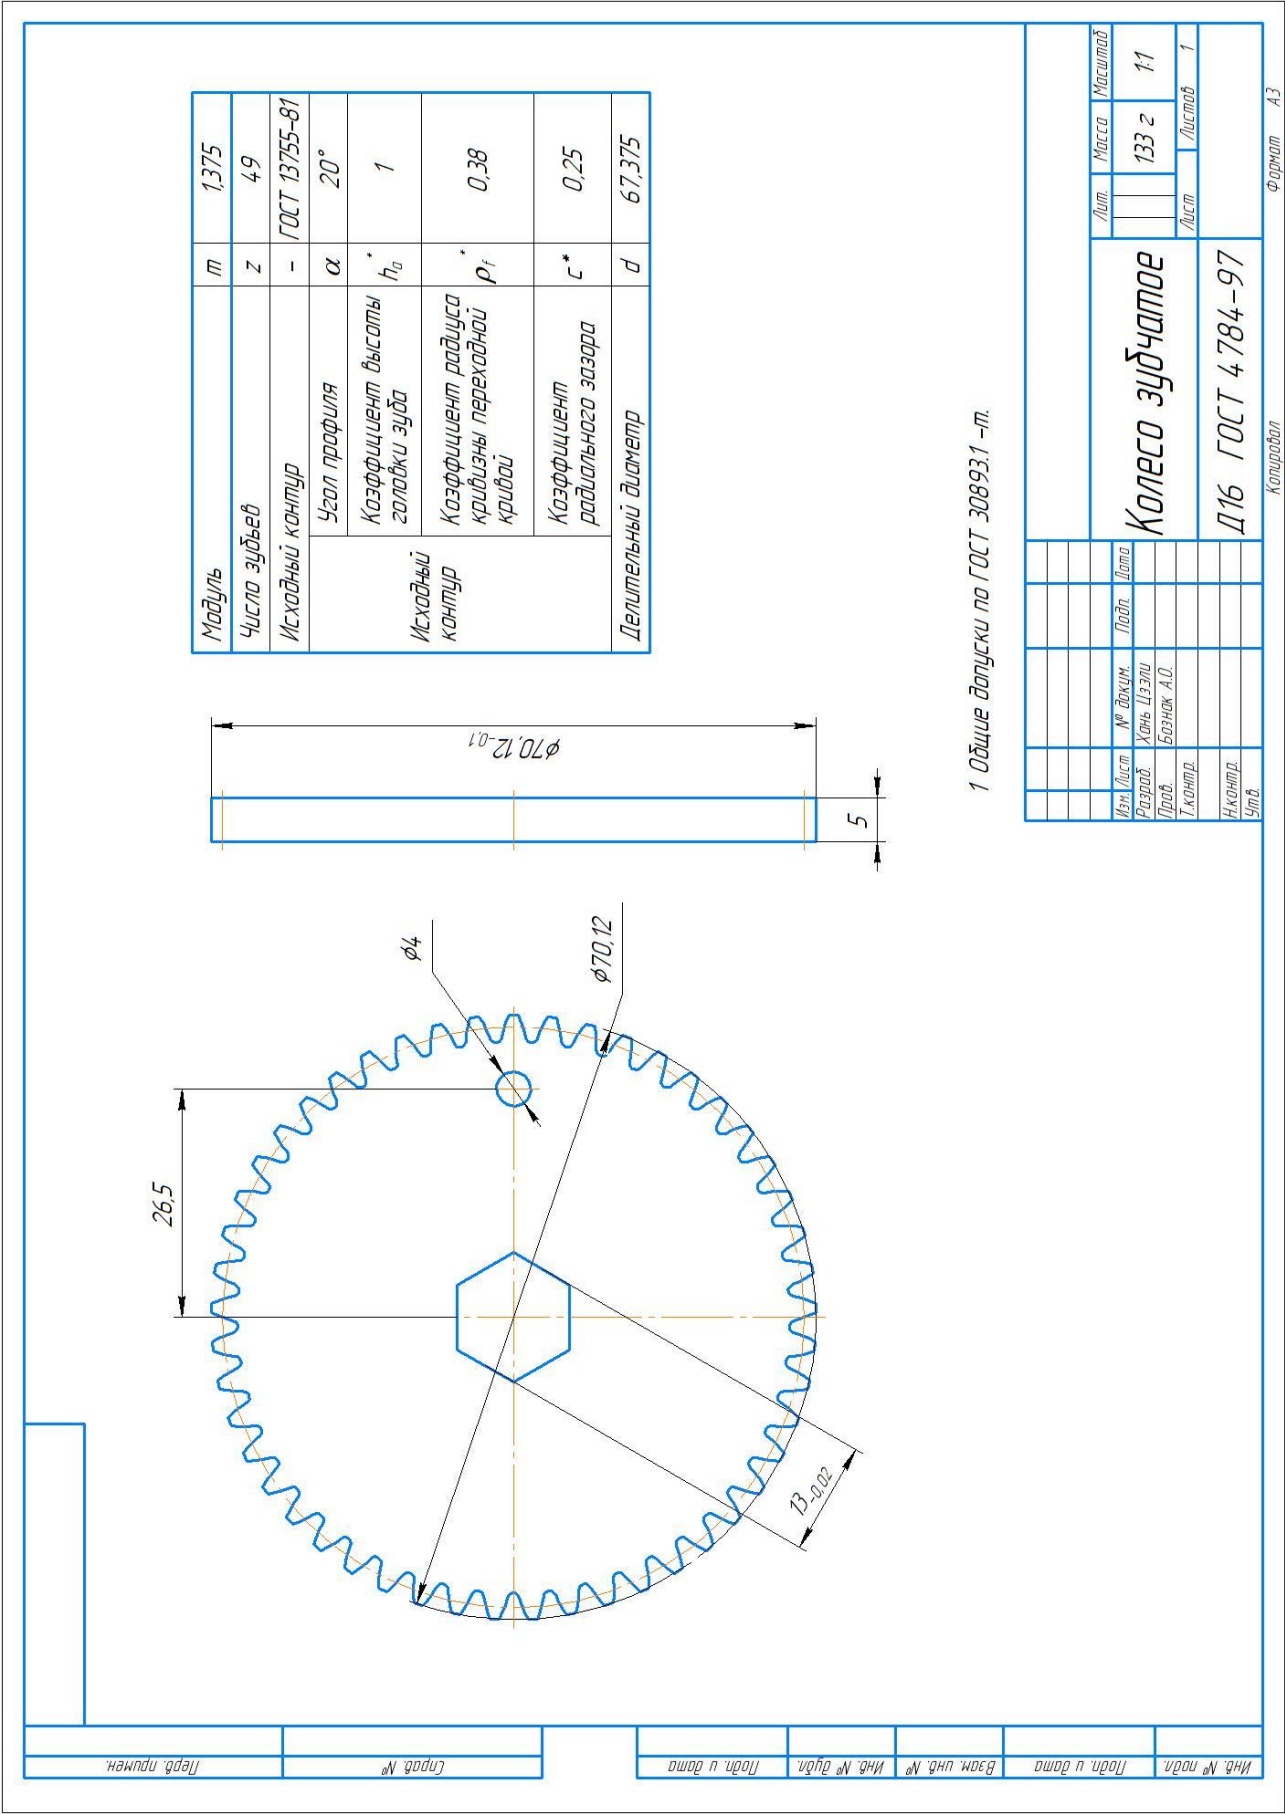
Чертеж детали «Колесо зубчатое»
